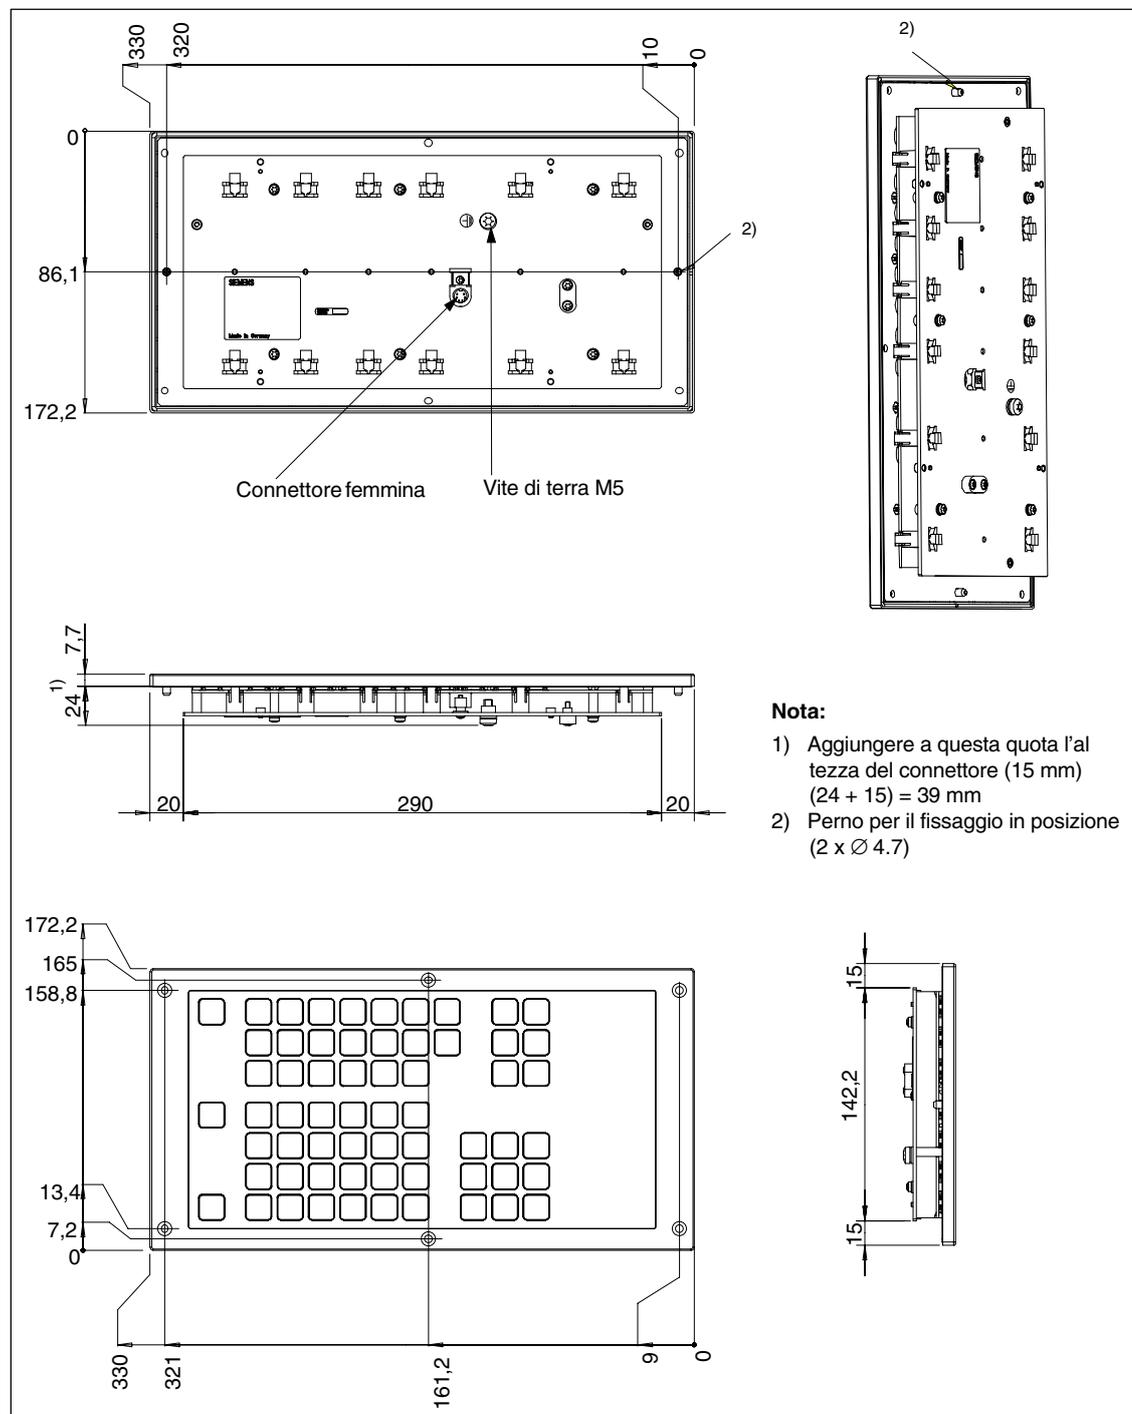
Disegno quotato della tastiera CN (montaggio accanto alla PCU)
